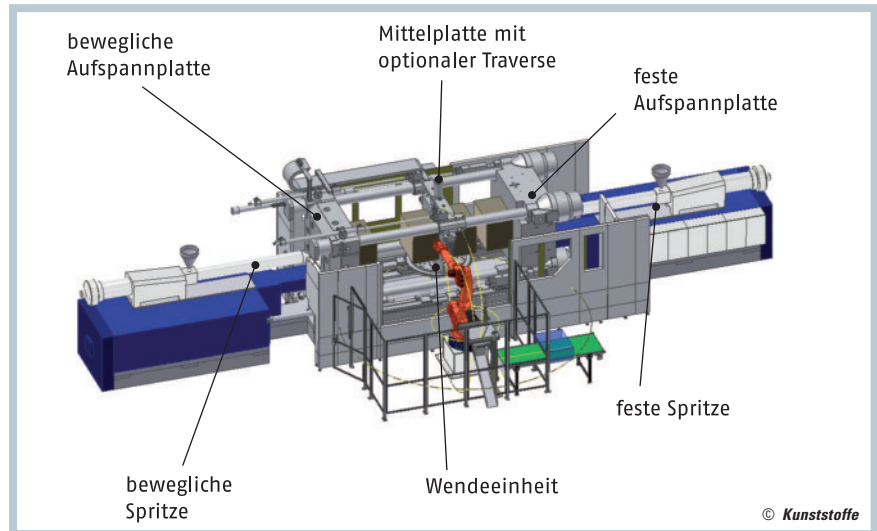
Ein Konzept für eine SpinForm-Maschine mit Automation: Die Einspritzaggregate stehen sich in der Maschinenachse gegenüber und die Wendeeinheit wird über das obere Holmenpaar zusätzlich geführt
